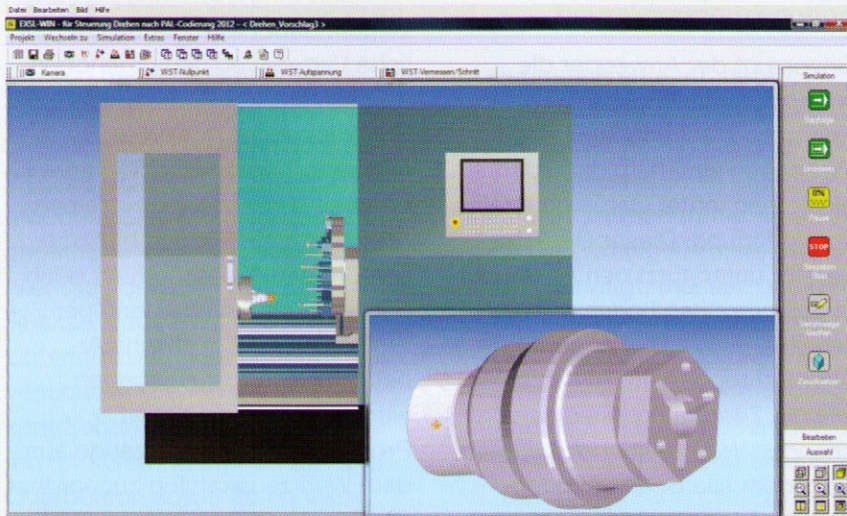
Drehbearbeitung mit C-Achse und angetriebenen Werkzeugen
